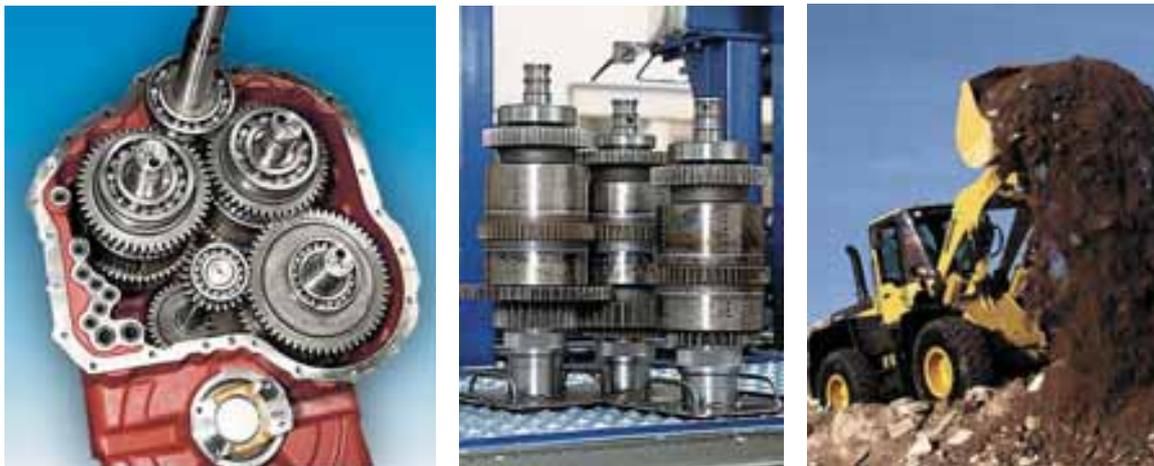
, 120, 121: Getriebeeinheit für einen Radlader.
